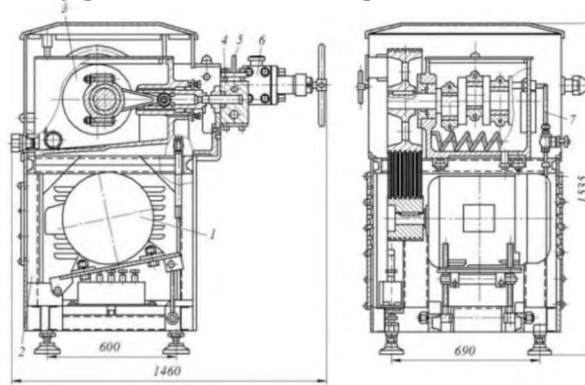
Конструкція гомогенізатора А1- ОГМ 1 – електродвигун; 2 – станина; 3 – кривошипно - шатунний механізм; 4 – плунжерний блок; 5 – манометрична головка; 6 – гомогенізуюча головка; 7 – система змащення та охолодження.
